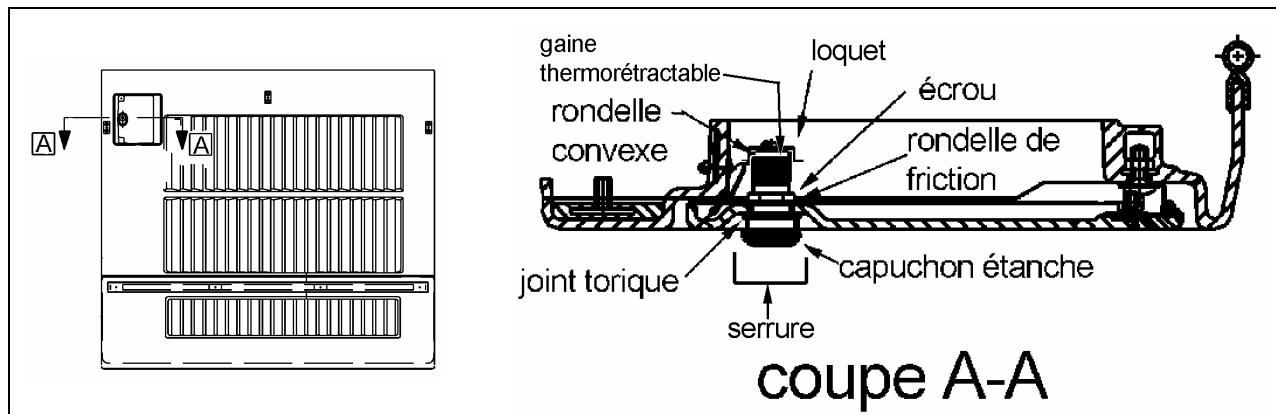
PETITE PORTE D'ACCÈS AU COL DE REMPLISSAGE DE CARBURANT
